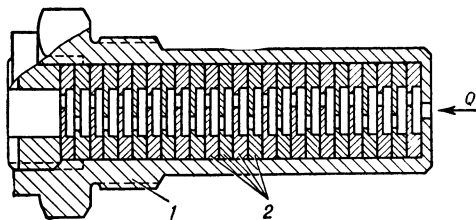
Конструкция пакета дросселирующих шайб: 1 — корпус; 2 — шайбы.
